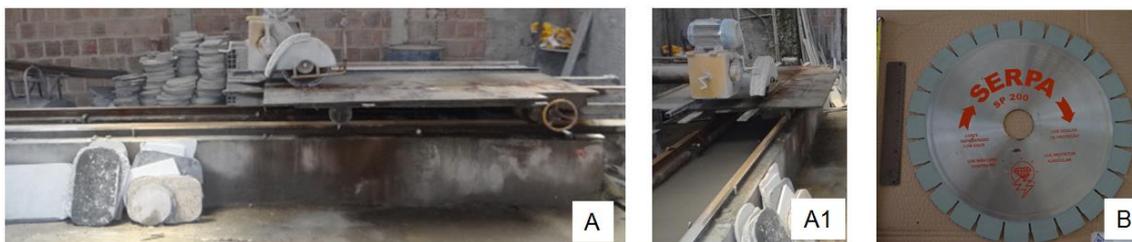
A) Máquina de Corte; A1) Detalhe do Tanque de efluente; B) Disco Diamantado.
